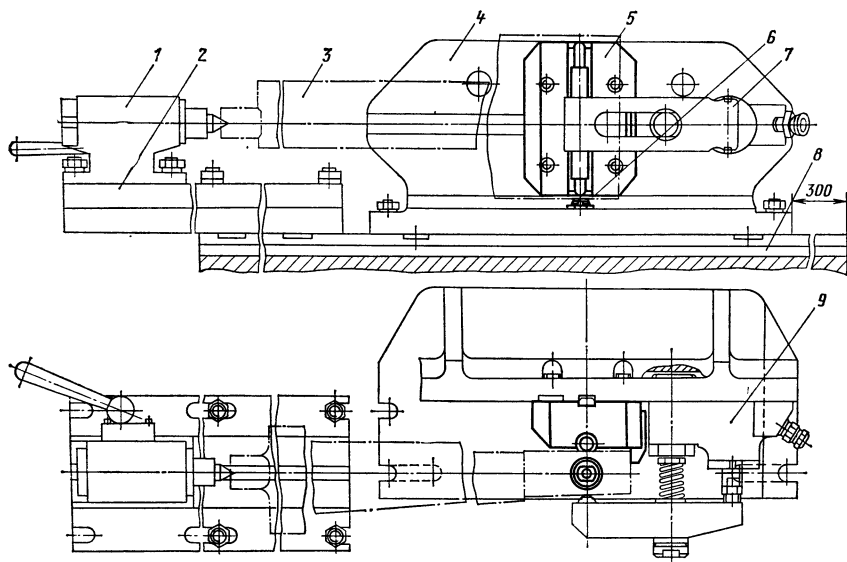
Специализированное наладочное приспособление для фрезерования входной и выходной плоскостей хвоста рабочих лопаток
